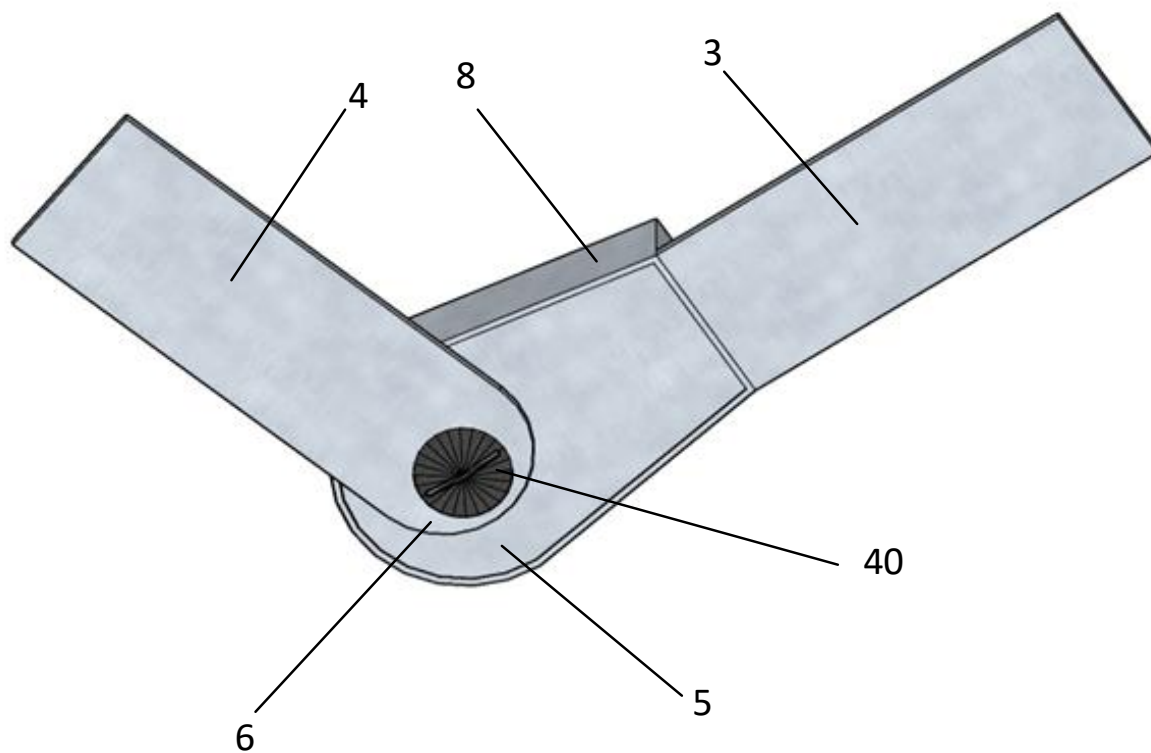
Фрагмент з'єднання коробчастого корпусу механізму редресації з шинами плеча і передпліччя, вигляд з внутрішнього боку.
